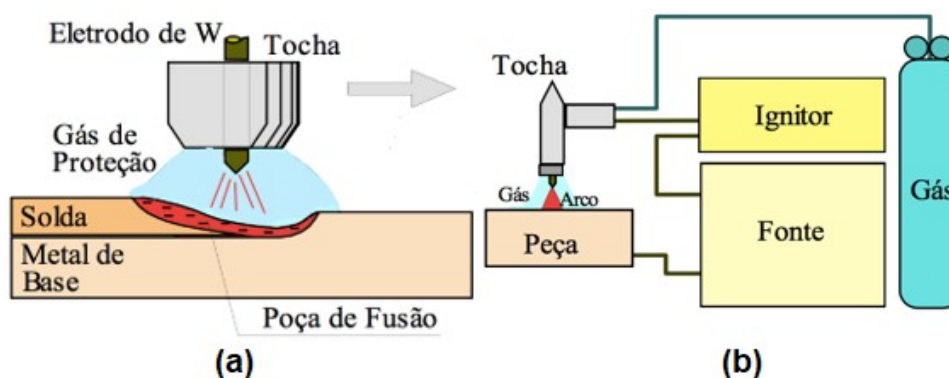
Representação esquemática do processo de soldagem GTAW (modificada): (a) detalhe da região do arco, (b) montagem usual.
